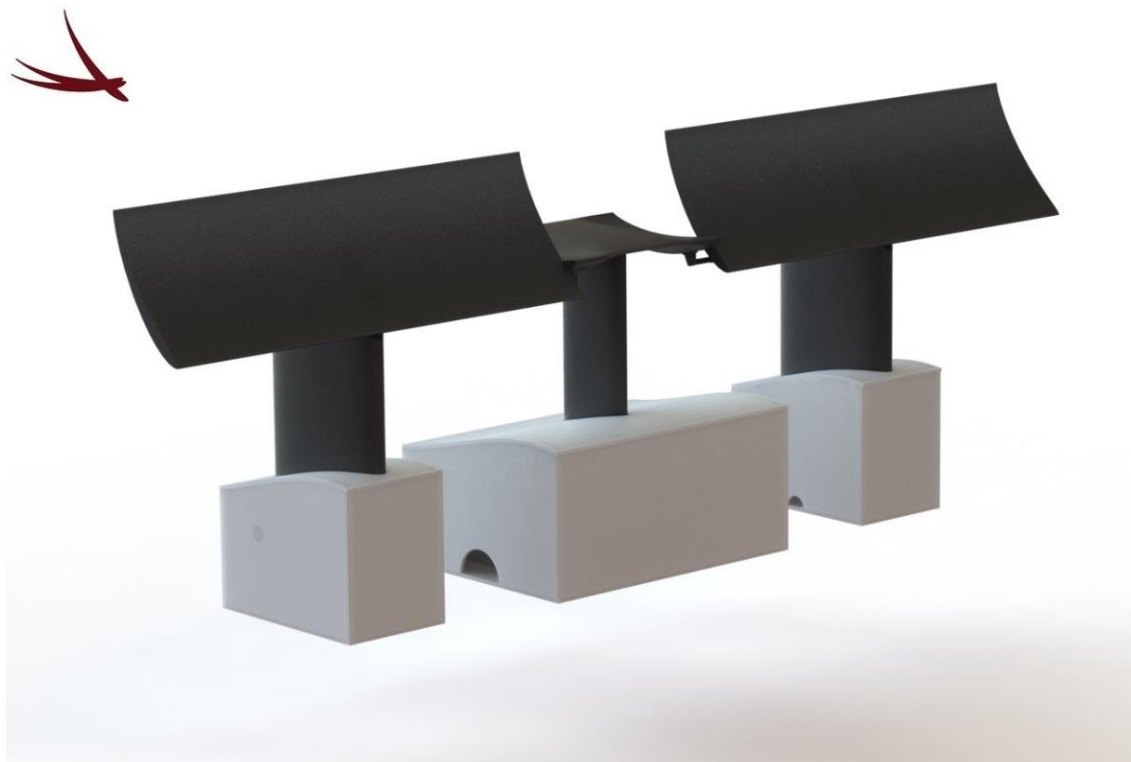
Vista isométrica del modelo CAD renderizado de la maqueta.
